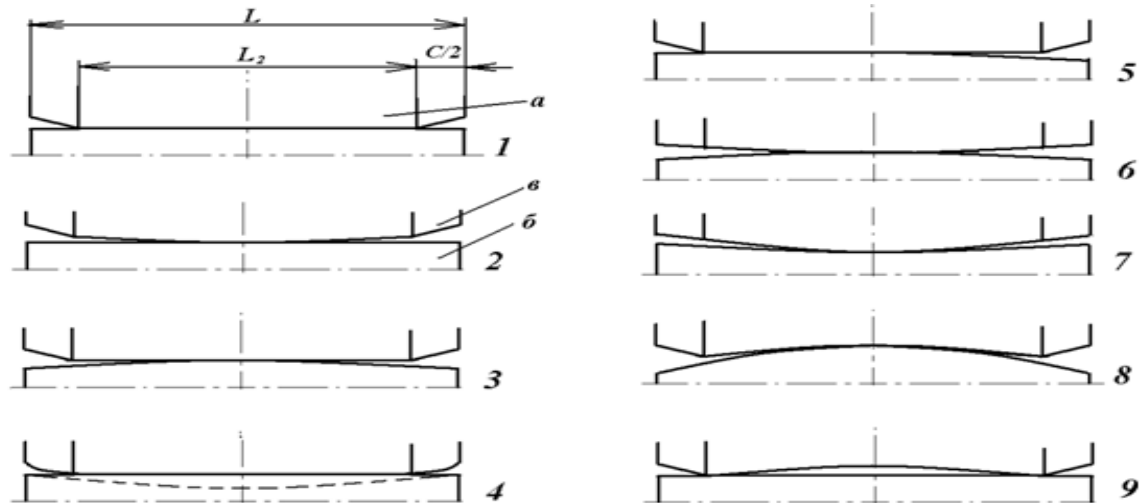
Виды профилировок (форм образующих) валков. а - опорный валок; б - рабочий валок; в - скос (врез)
